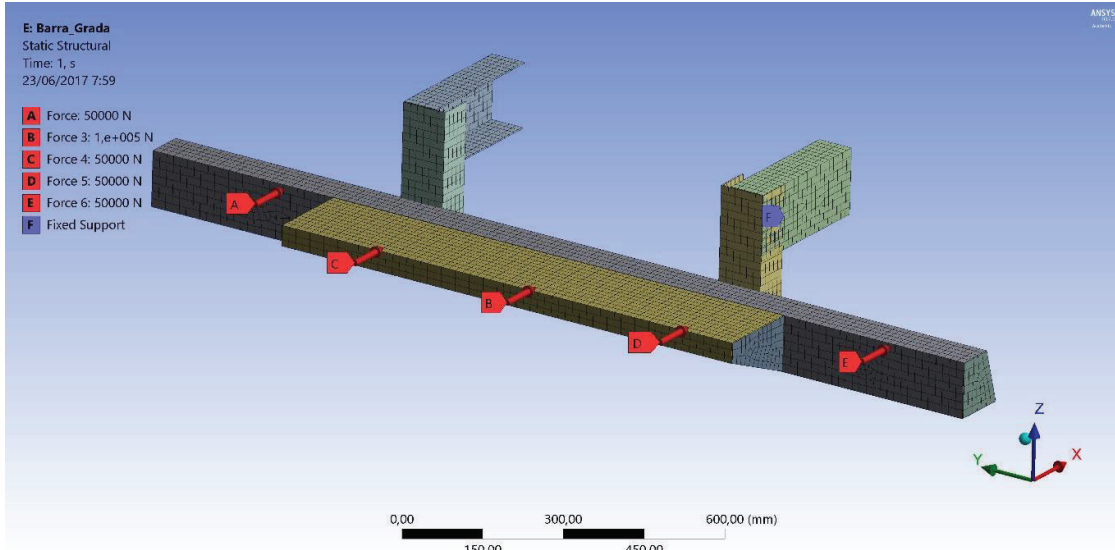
Modelado del dispositivo antiempotramiento de plancha corrugada tipo grada.
